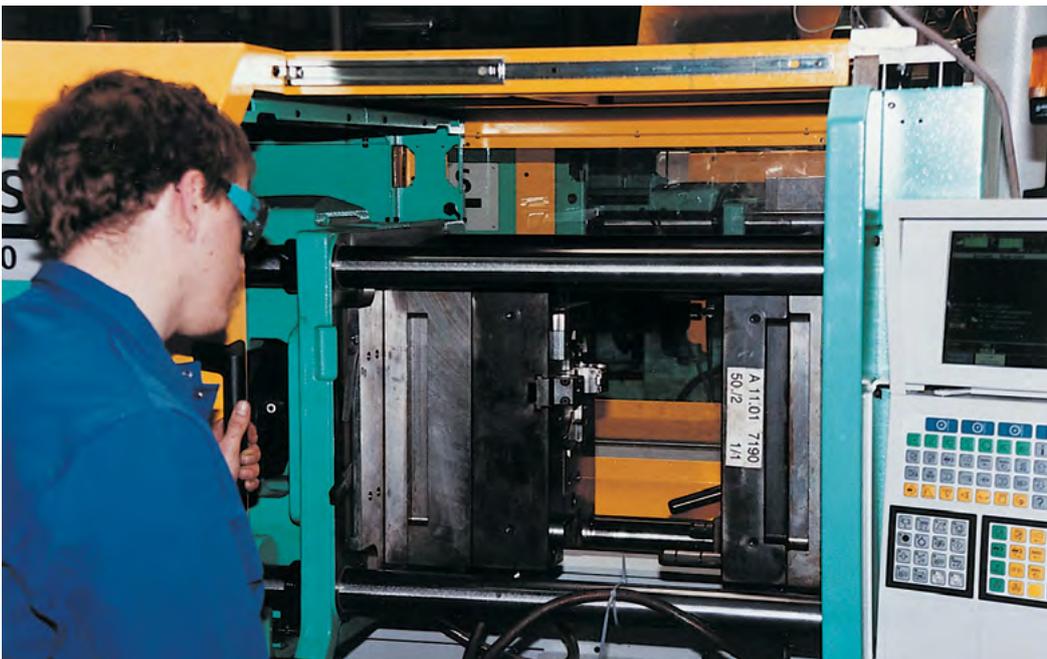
Blick in den geöffneten Werkzeugbereich
